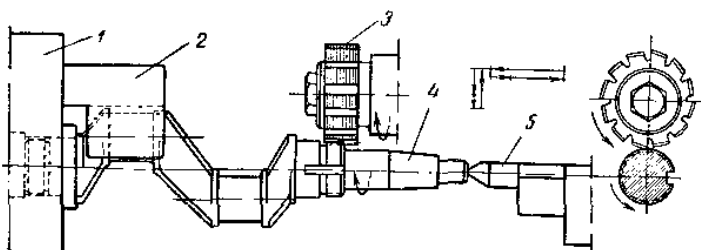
Наладка резьбофрезерного станка для фрезерования резьбы на коленчатом валу:
